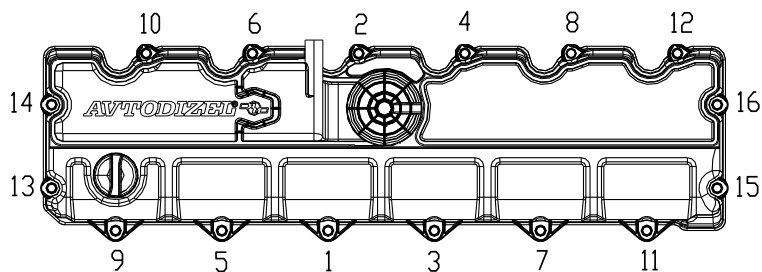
Порядок затяжки болтов крепления крышки головки цилиндров
